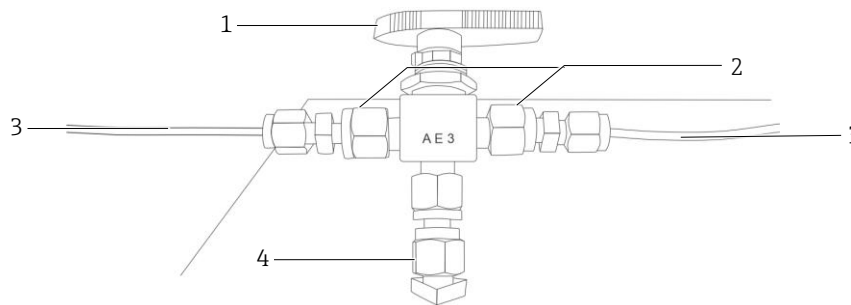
Anschlüsse für die Gaszufuhr mit Probenaufbereitungssystem
